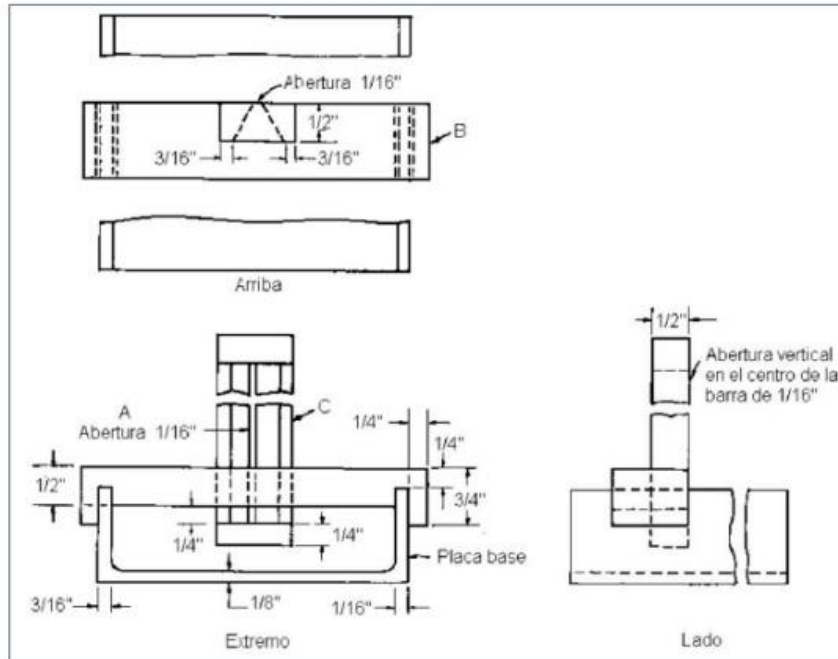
Detalle en planta del equipo adecuado para la determinación del diámetro final usado para el alineamiento del espécimen.
